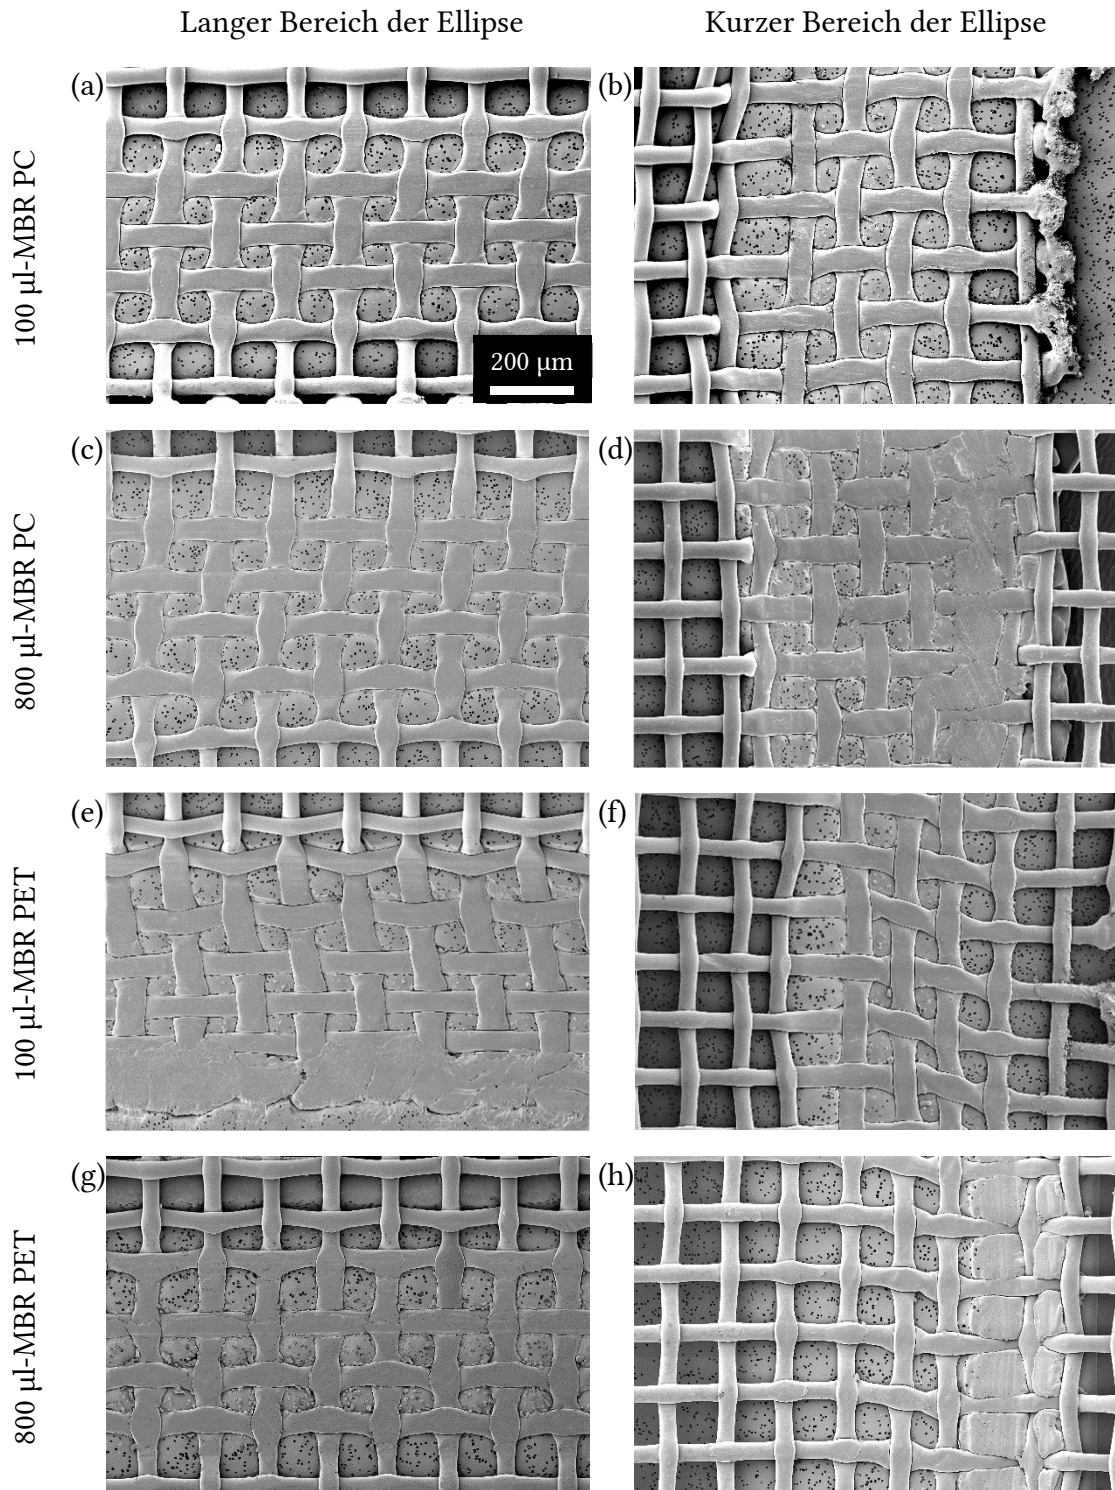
REM-Aufnahmen der Schweißnähte vom Ultraschallschweißen von Membran und PET-Gewebering auf die Chiphälfte mit Zellkammer. (a-b) Schweißnaht am 100 μl -MBR aus PC, (c-d) Schweißnaht am 800 μl -MBR aus PC, (e-f) Schweißnaht am 100 μl -MBR aus PET, (g-h) Schweißnaht am 800 μl -MBR aus PET. Der Maßstabsbalken 200 μm gilt für alle Aufnahmen.
